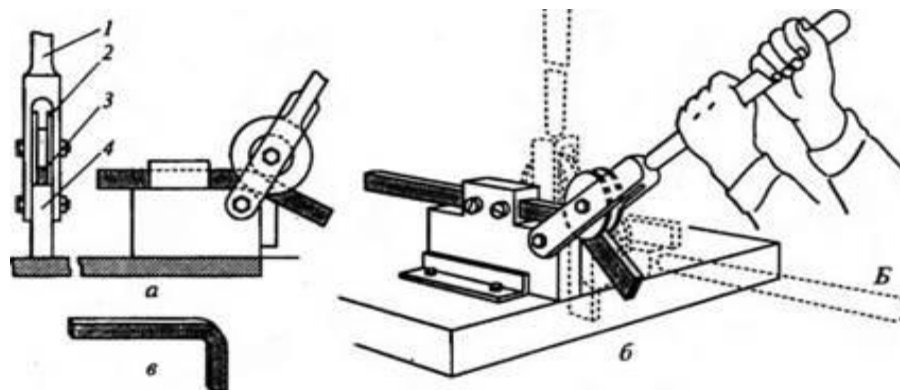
Приспособление для гибки рамки ножовочного станка:
